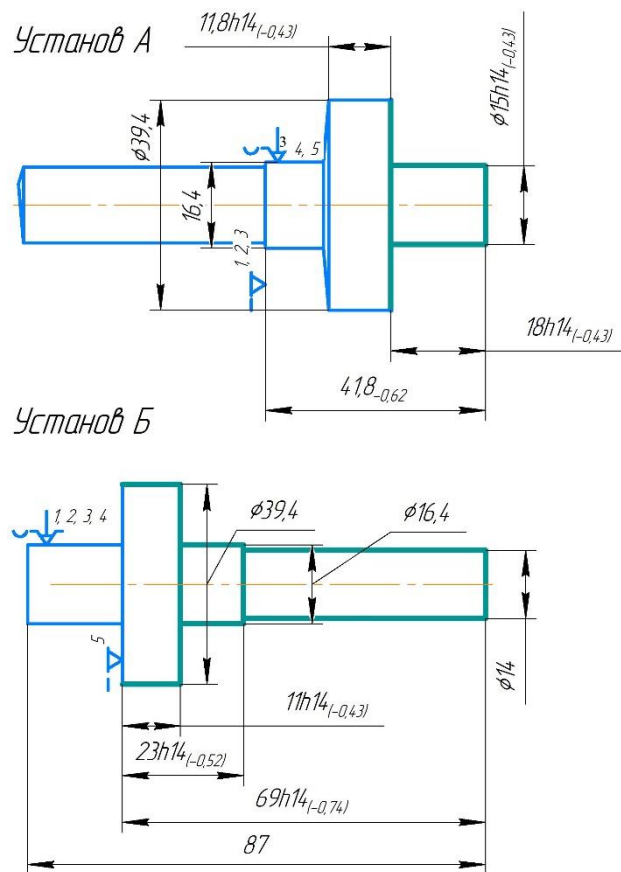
Базування заготовки на операції 015 по схемі №2
